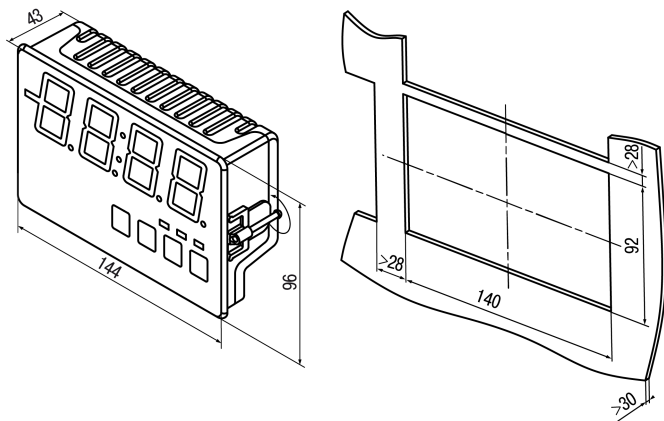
Габаритные размеры корпуса Щ8
